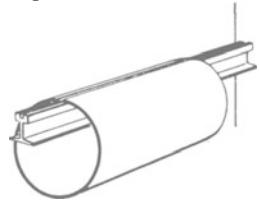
Schweißunterlage für Behältermäntel.
